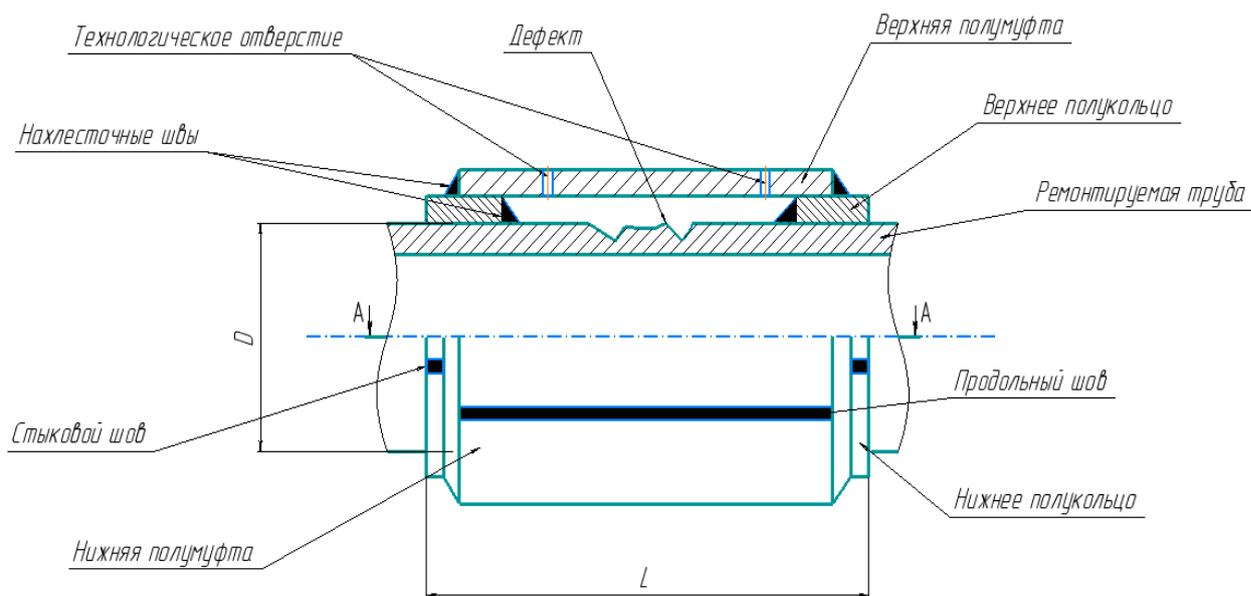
Герметичная стальная сварная муфта конструкции №3
